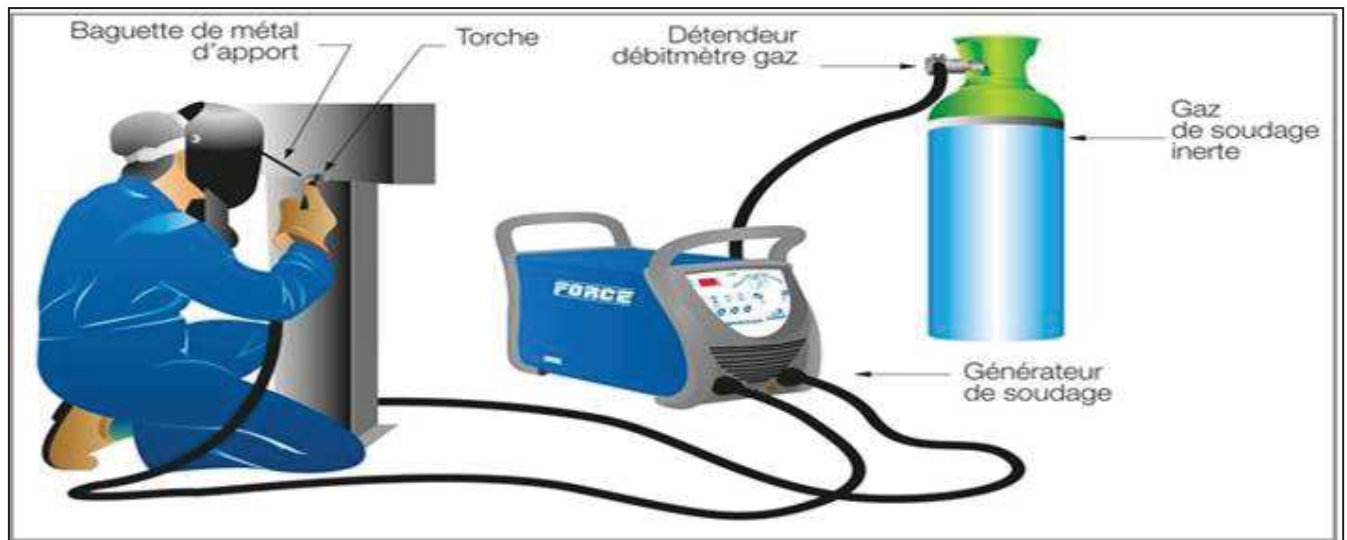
Installation manuelle pour soudage TIG [2]
